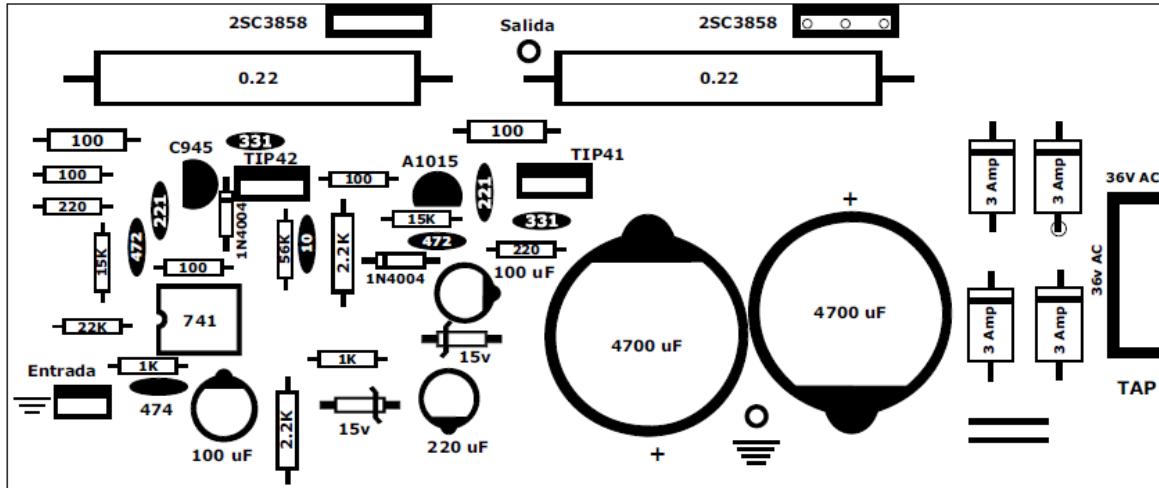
Posición de los componentes electrónicos sobre la PCB.
